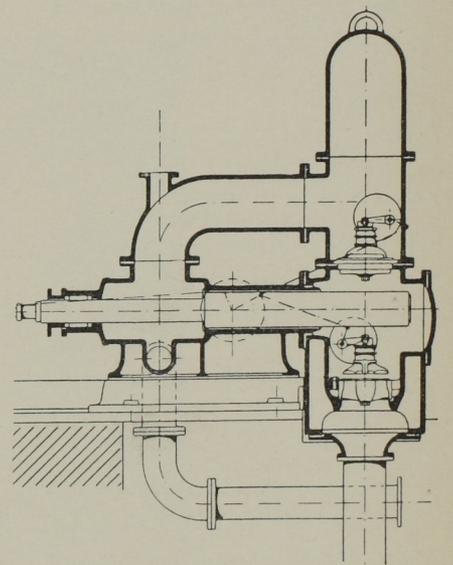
Seitenansicht der Pumpmaschine. Masst. 1:30.
